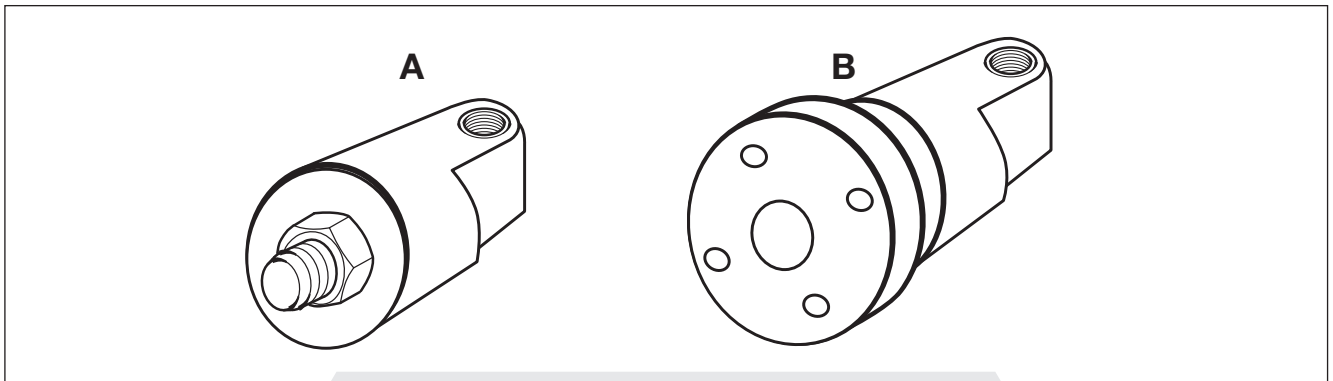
Varianten für die Befestigung an die Maschinenwelle
